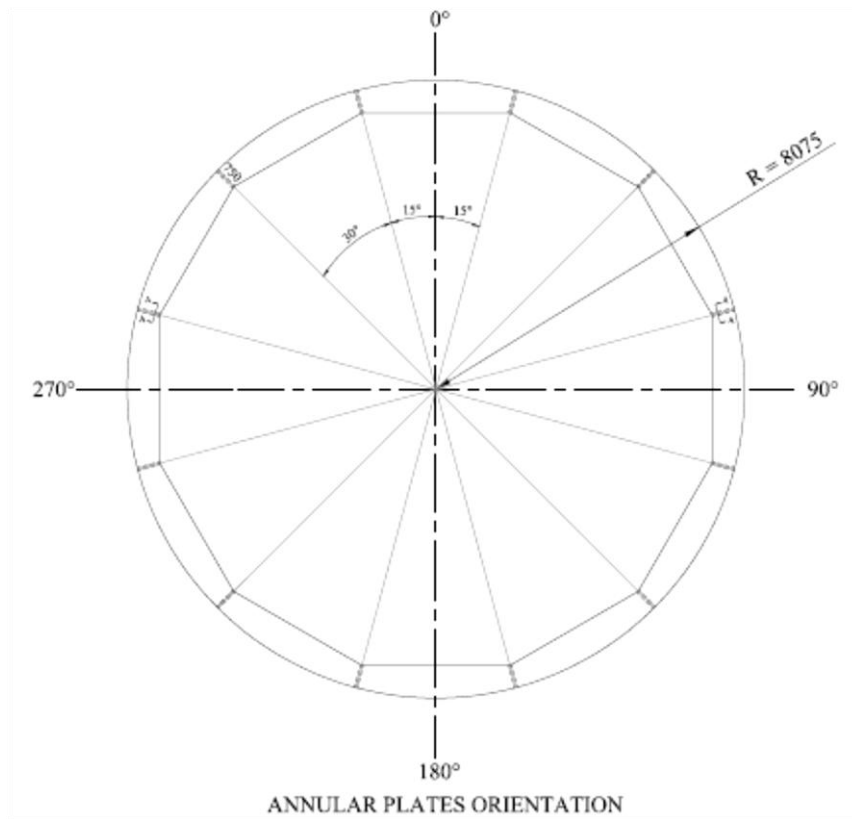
Disposizione e forma lamiere anello più esterno piastra di base
